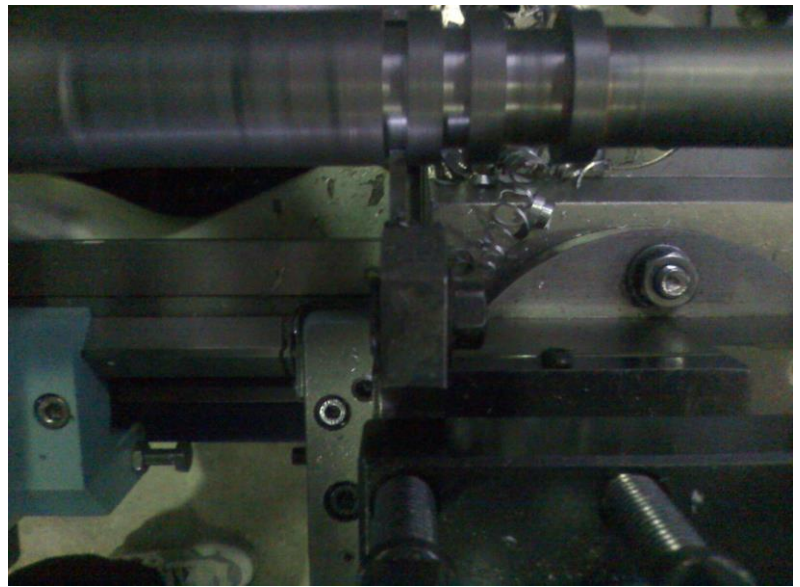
Alargamento do canal, lado esquerdo.
